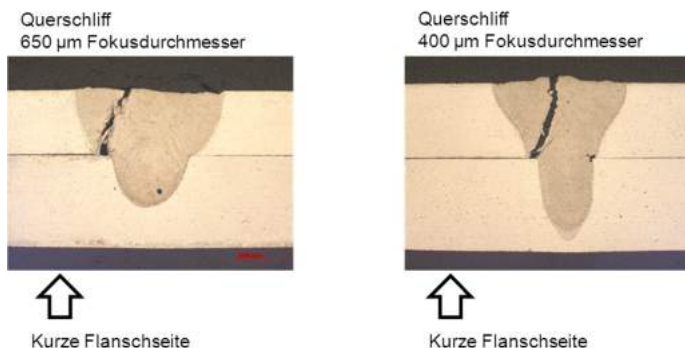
Links: Querschliff einer Schweißnaht erzeugt beim randnahen Schweißen mit 650 µm Fokusschmelldurchmesser bei 4 mm Randabstand.
